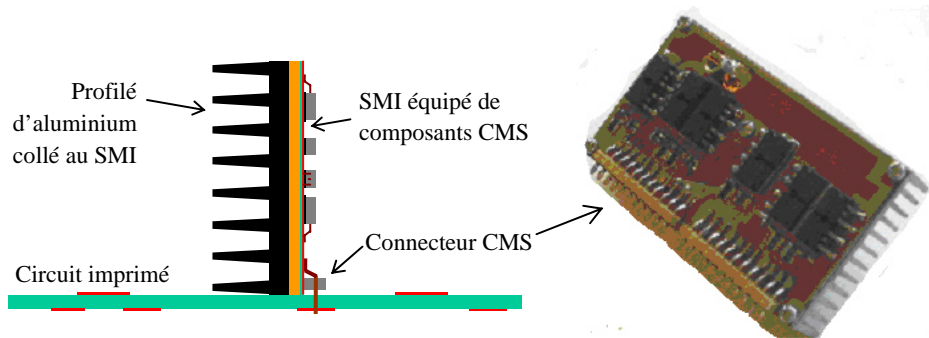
Exemple de SMI soudé perpendiculairement sur un circuit imprimé
